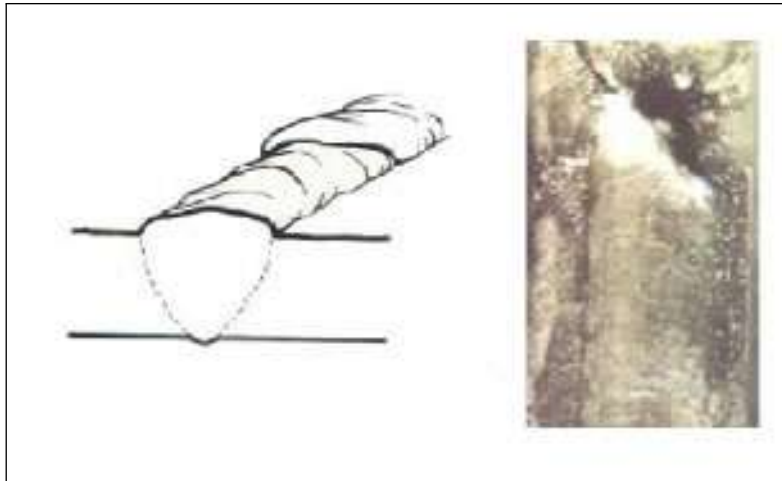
Falta de continuidad en el cordón de soldadura.
